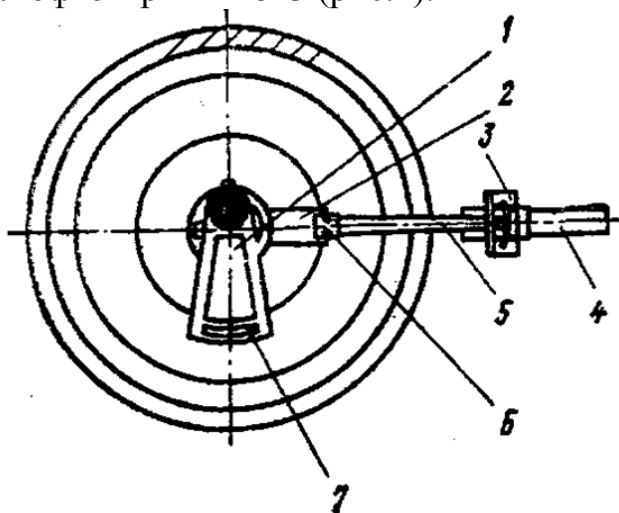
Установка люфтометра КИ-4813 на піввісь ведучого колеса колісного трактора: 1 - корпус; 2 - змінна головка; 3 - шкала динамометричного важеля; 4 - рукоятка динамометричного важеля; 5 - стрілка динамометричного важеля; 6 - вороток; 7 - шкала показчика зазору.
